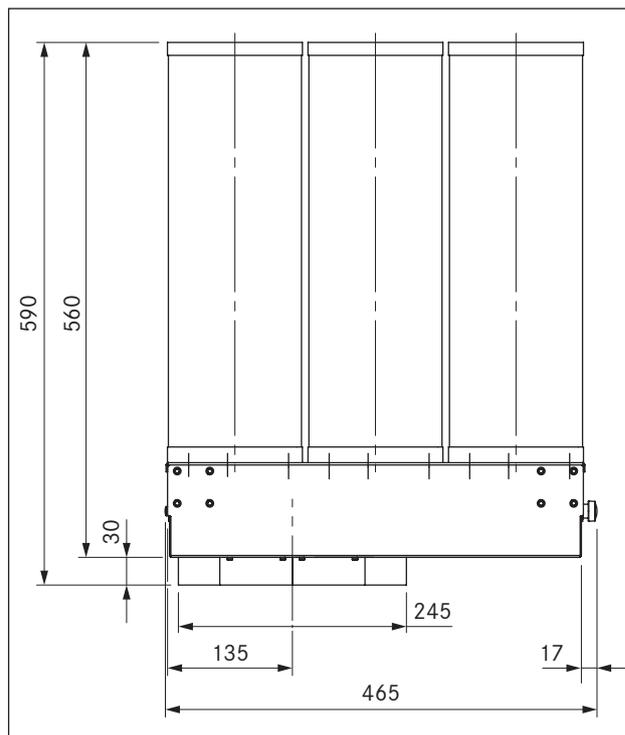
ULB3 dimensiones del aparato vista frontal
